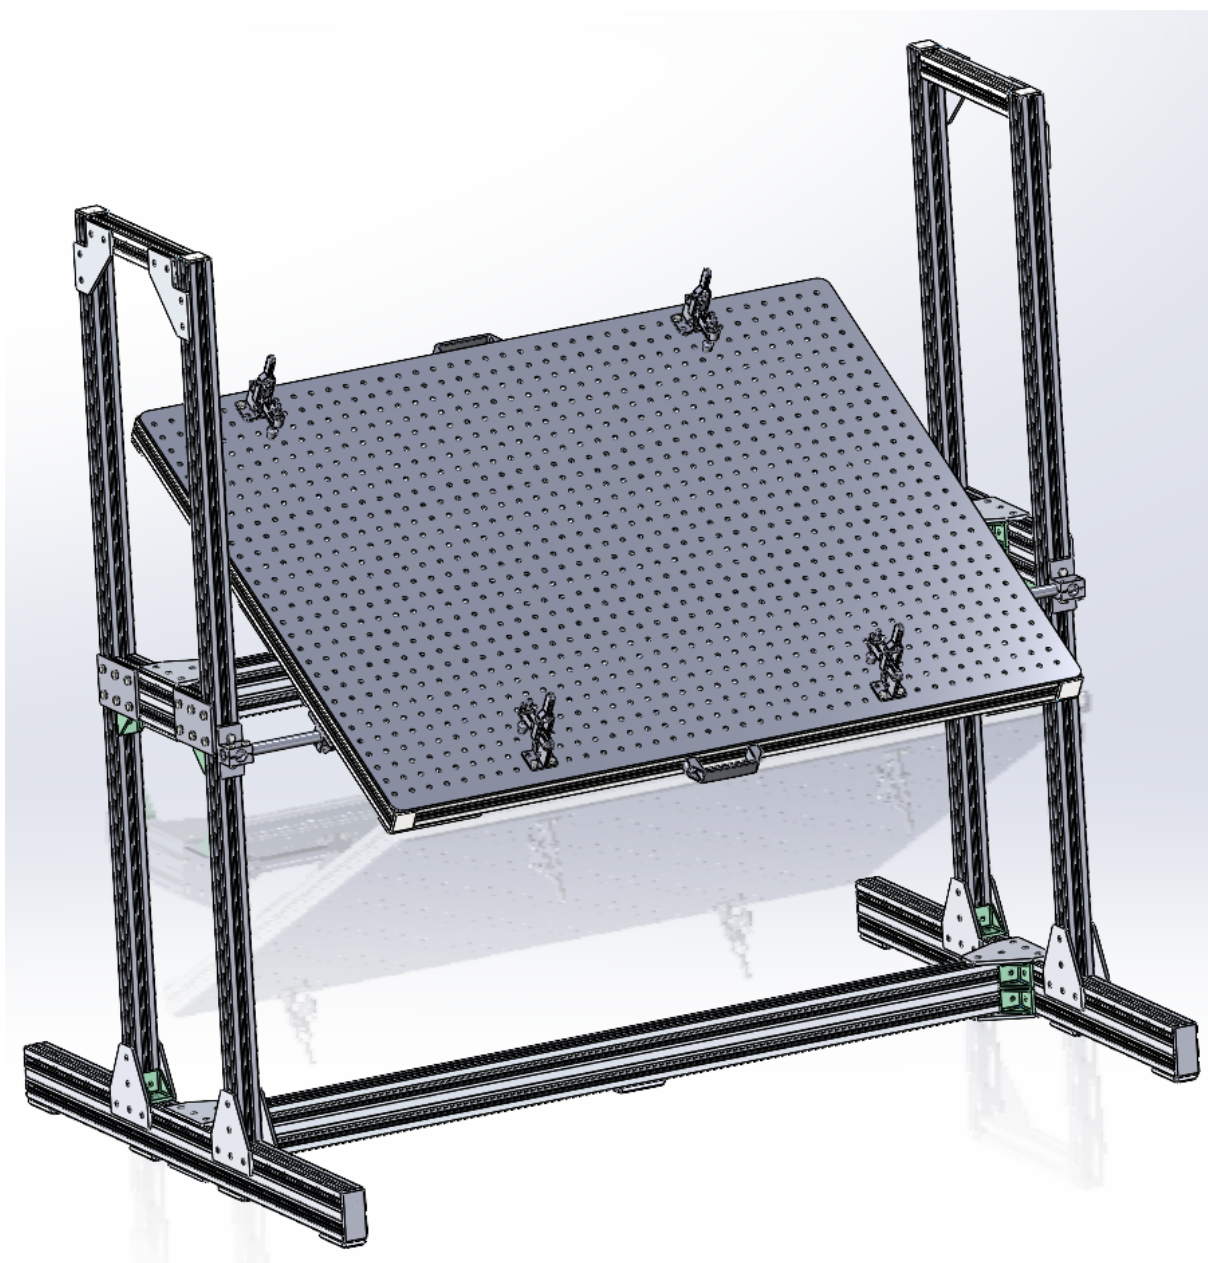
3D модель розробленого пристрою для виконання зварювальних робіт.
